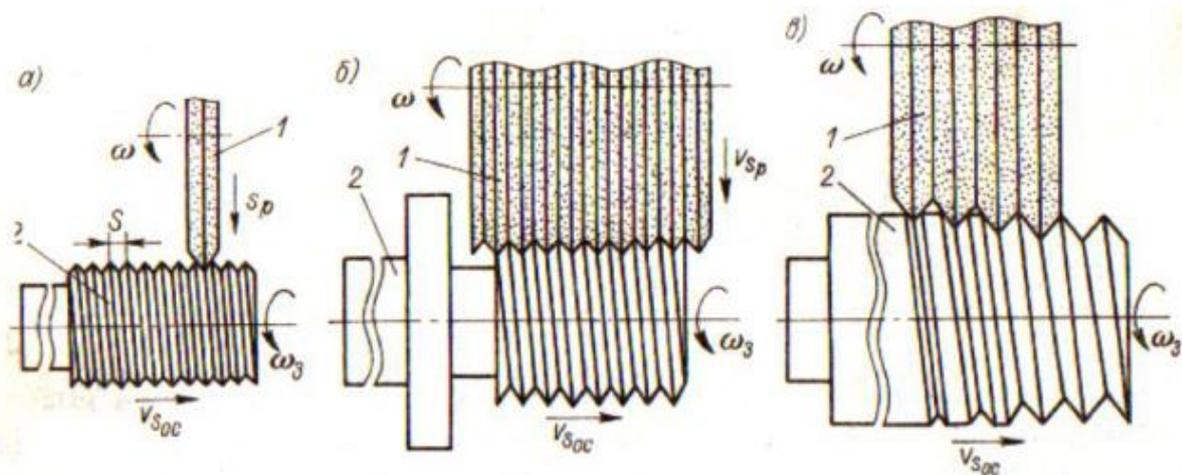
Схема резьбошлифования: 1 – шлифовальный круг; 2 - заготовка
